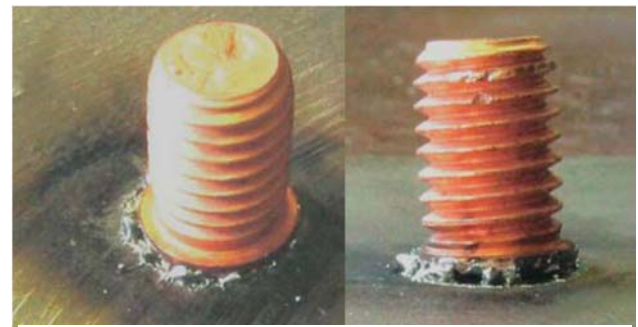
Soldaduras inaceptables debido a una energía de soldeo demasiado elevada (izquierda) o demasiado baja (derecha) en un soldeo al arco con ignición en la punta del espárrago.
